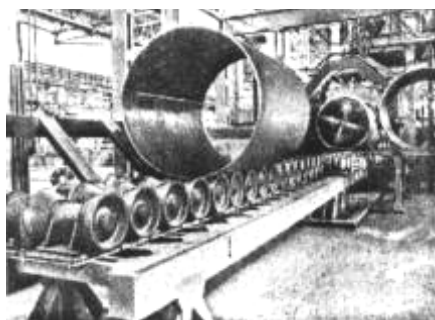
Сварной резервуар для хранения нефтепродуктов, работающий под давлением
